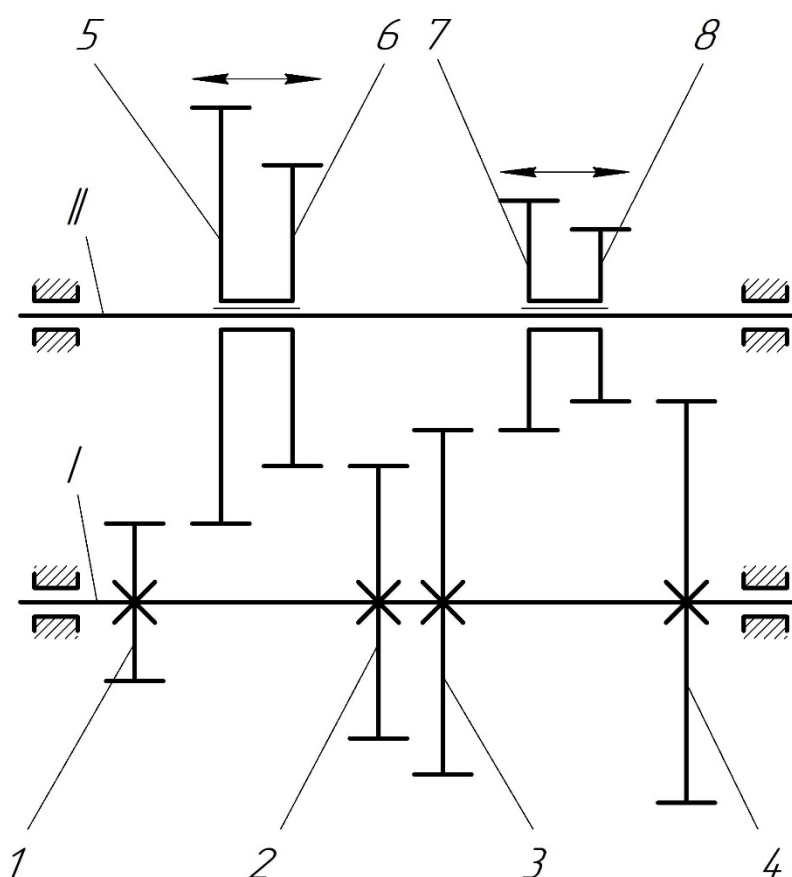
Схема четырехступенчатой коробки передач с двумя валами
